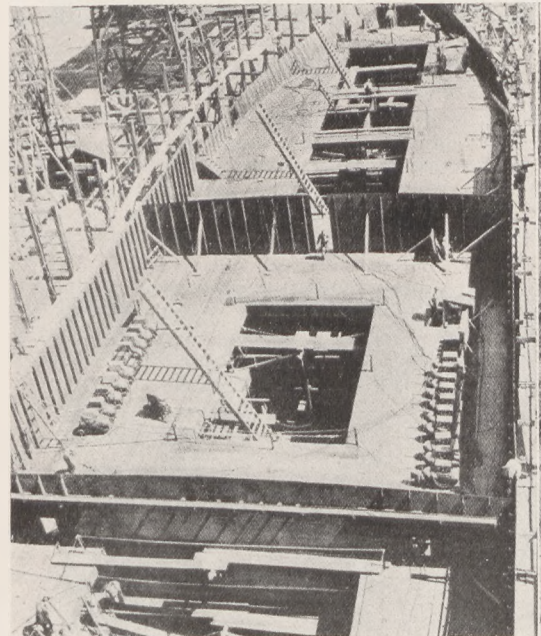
Montagestadium vor der Einbringung des Oberdecks (im Zwischendeck stehen 2 Batterien von Schweißmaschinen zu je 10 Stück).
